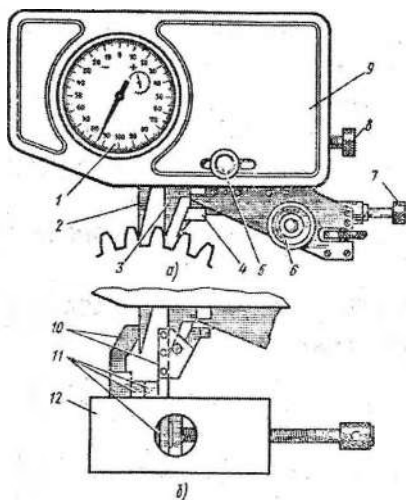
Шагомер для измерения шага зацепления: а — измерение шага зацепления; б — установка шагомера на размер и на «0» [10, с. 302]
